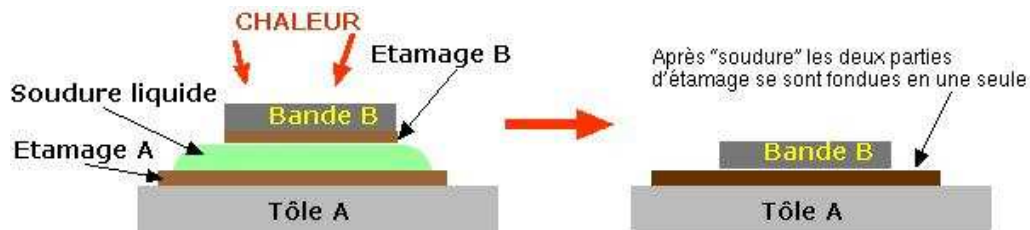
Assemblage de deux pièces « à plat » Fig 5
